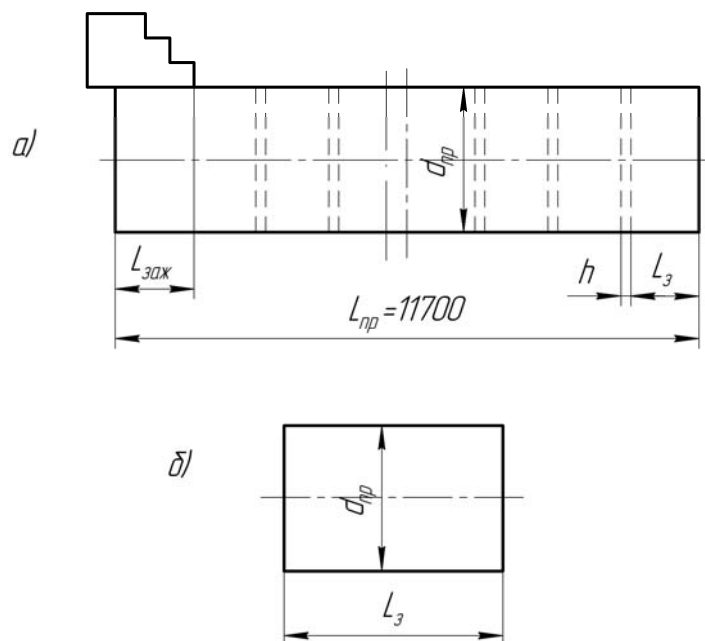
Схема разделки прутка (а) и эскиз заготовки (б)
